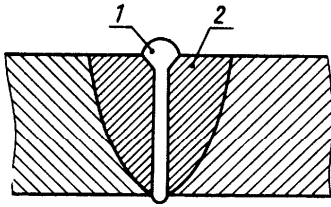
Форма шва при электронно-лучевой (1) и аргонодуговой (2) сварке
